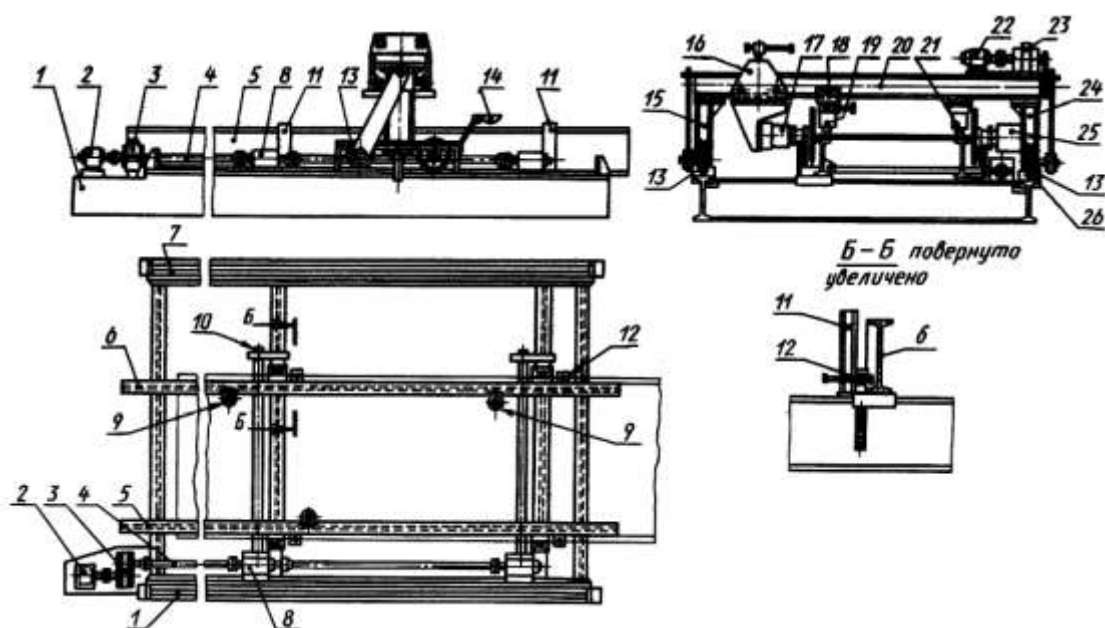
Установка для сборки двутавровых балок с самоходным сборочным порталом
